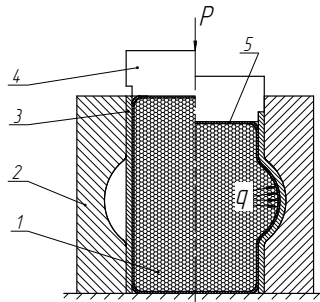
Схема пристрою для роздачі труби: 1 – наповнювач, 2 – напівматриці, 3 – трубчаста заготовка, 4 – пуансон, 5 – еластична оболонка
